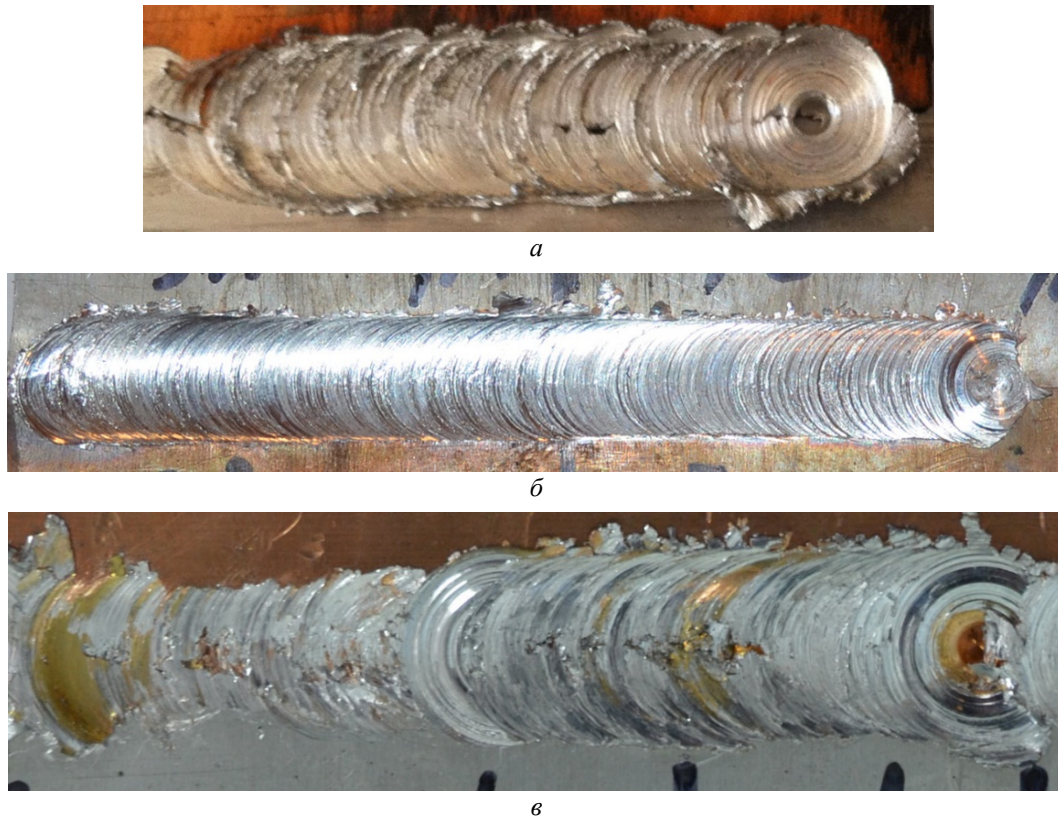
Морфология сварного шва при скорости сварки 25 мм/мин и угле наклона инструмента 3° от скорости вращения СИ об/мин:
